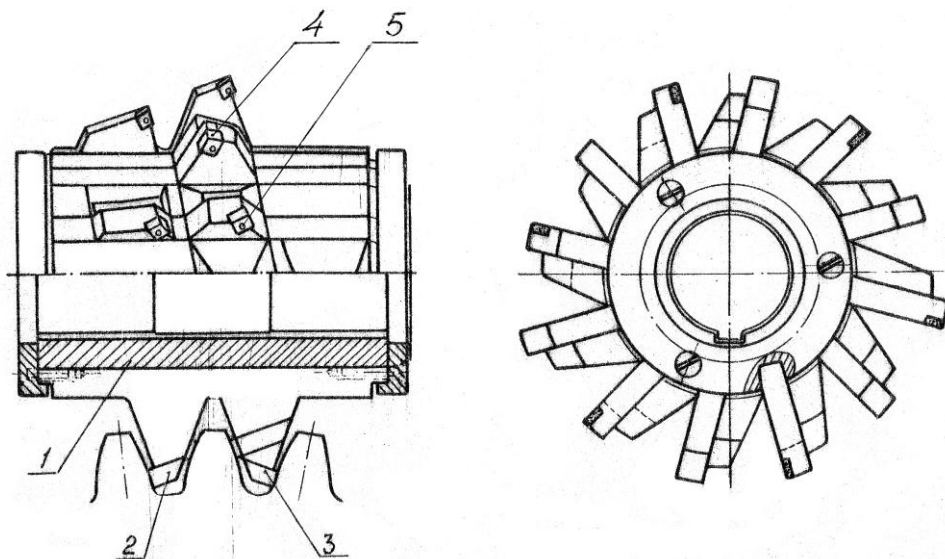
Твердосплавная фреза со вставными рейками, оснащенная неперетачиваемыми поворотными пластинками.
